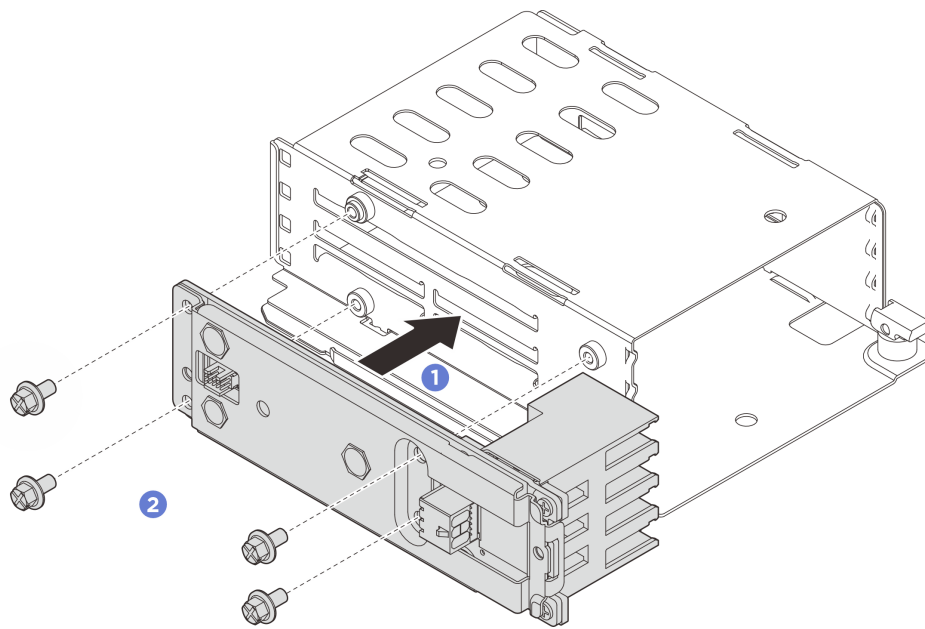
Installieren der Rückwandplattenbaugruppe
